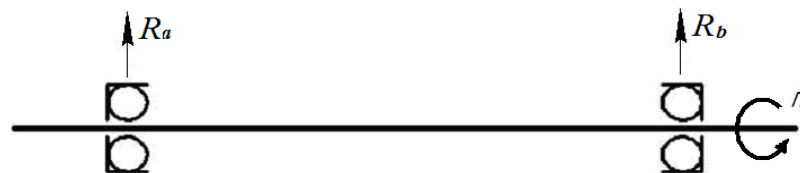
Схема для розрахунку підшипників в опорах вала
